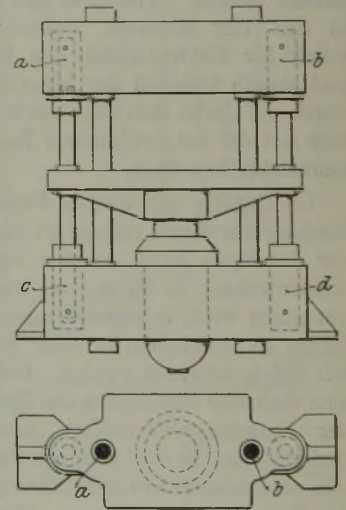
Hydraulische Parallel- oder Geradföhrung für Pressen und sonstige Maschinen. (Hydraulische Wage.)
